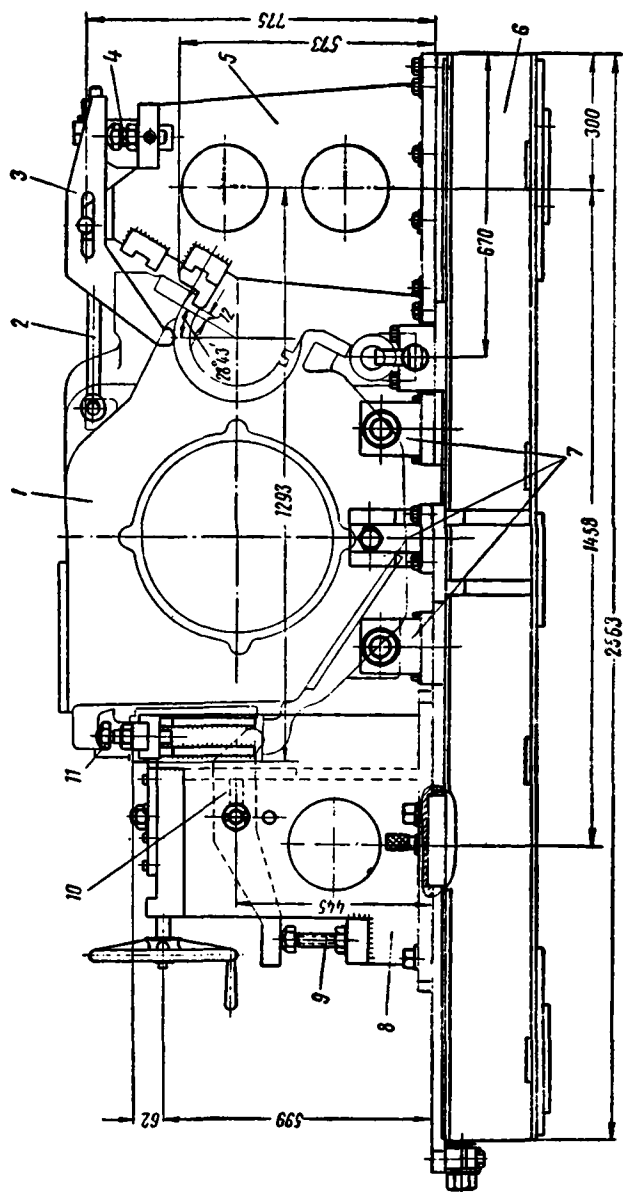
Приспособление для расточки горловины остовов тяговых двигателей НБ-411:
